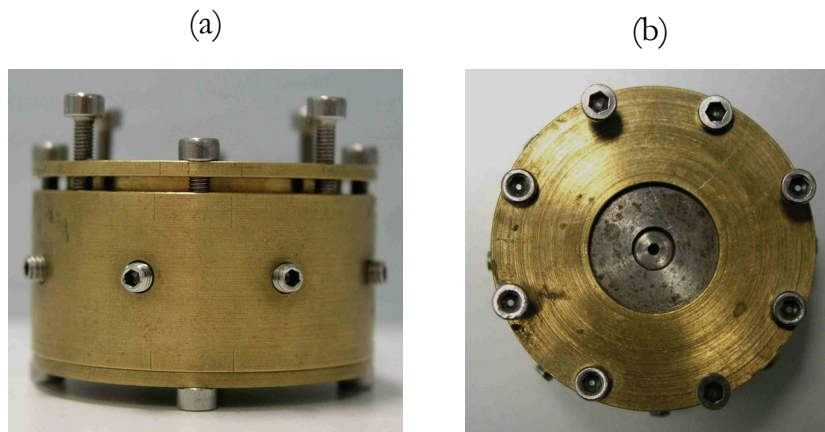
Aperçu de la structure fabriquée par la technique de l'assemblage mécanique, (a) vue de côté, (b) vue de dessus.
